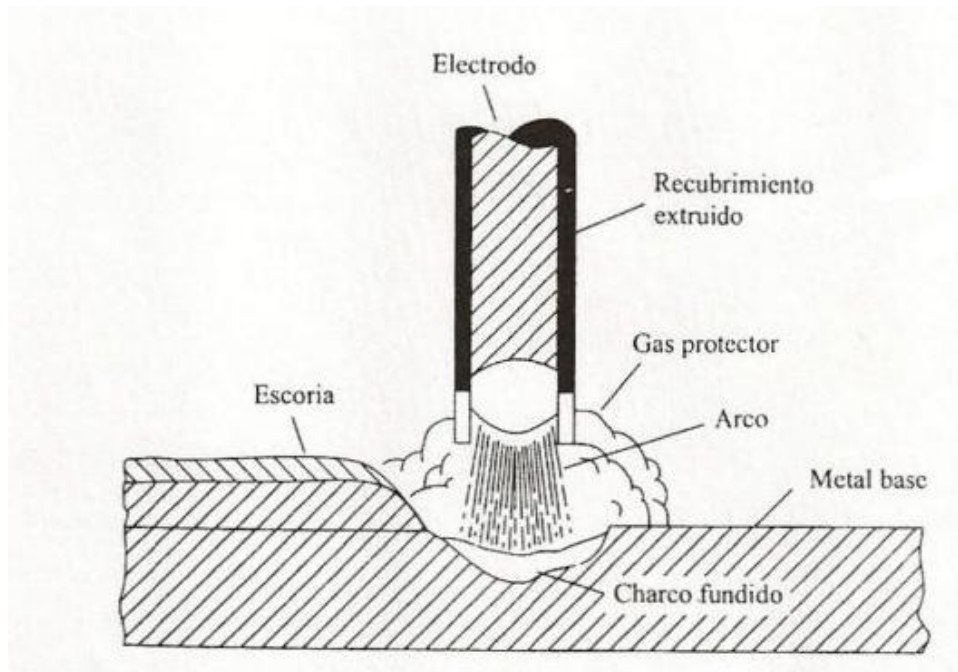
Como trabaja una soldadura. (Fuente: McCormac;2002;437)
